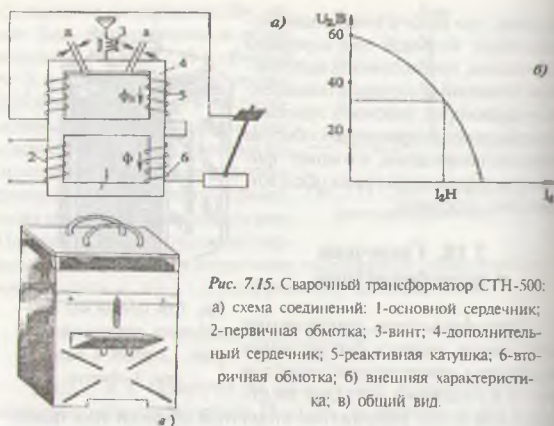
Сварочный трансформатор СТН-500: а) схема соединений: 1-основной сердечник; 2-первичная обмотка; 3-винт; 4-дополнительный сердечник; 5-реактивная катушка; 6-вторичная обмотка; б) внешняя характеристика; в) общий вид.
